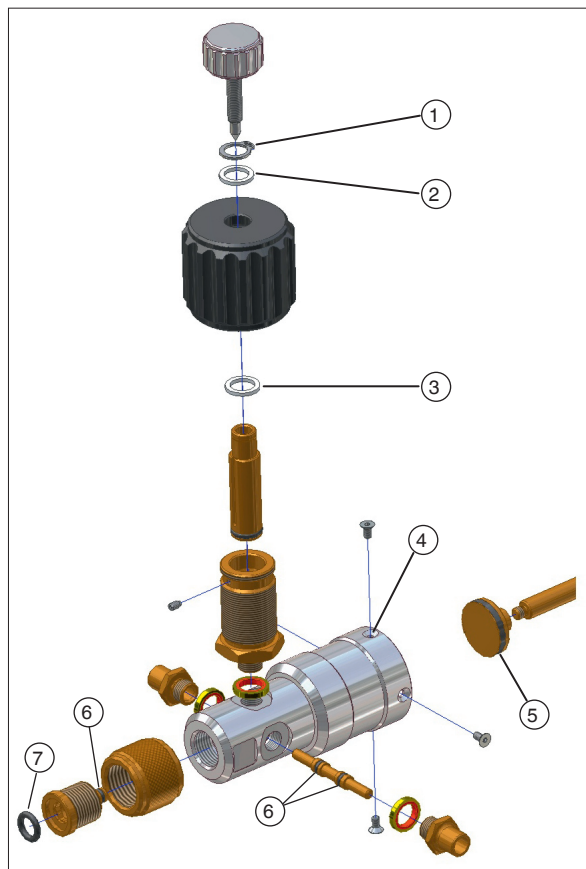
Montaż pierścieni, tarcz uszczelniających i o-ringów
